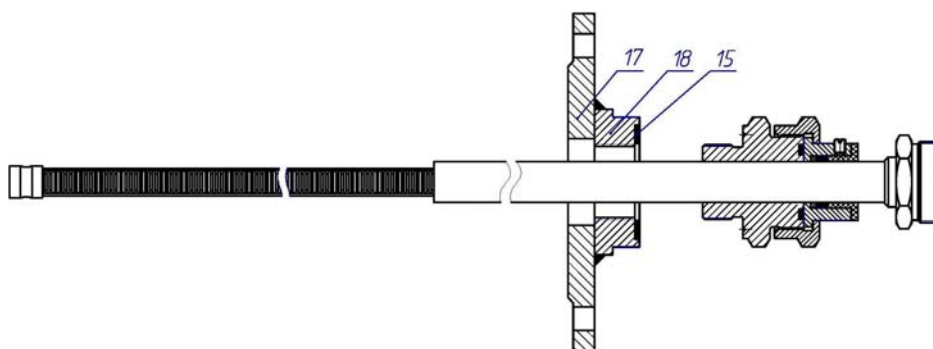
Установка прокладки и крышки фланца с бобышкой
